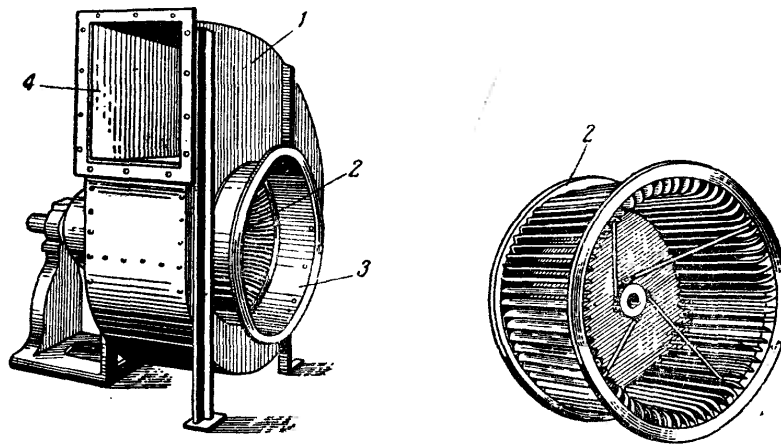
Відцентровий вентилятор Сірокко: 1 - кожух; 2 – робоче колесо; 3 – всмоктувальний патрубок; 4 – нагнітальні патрубок.
